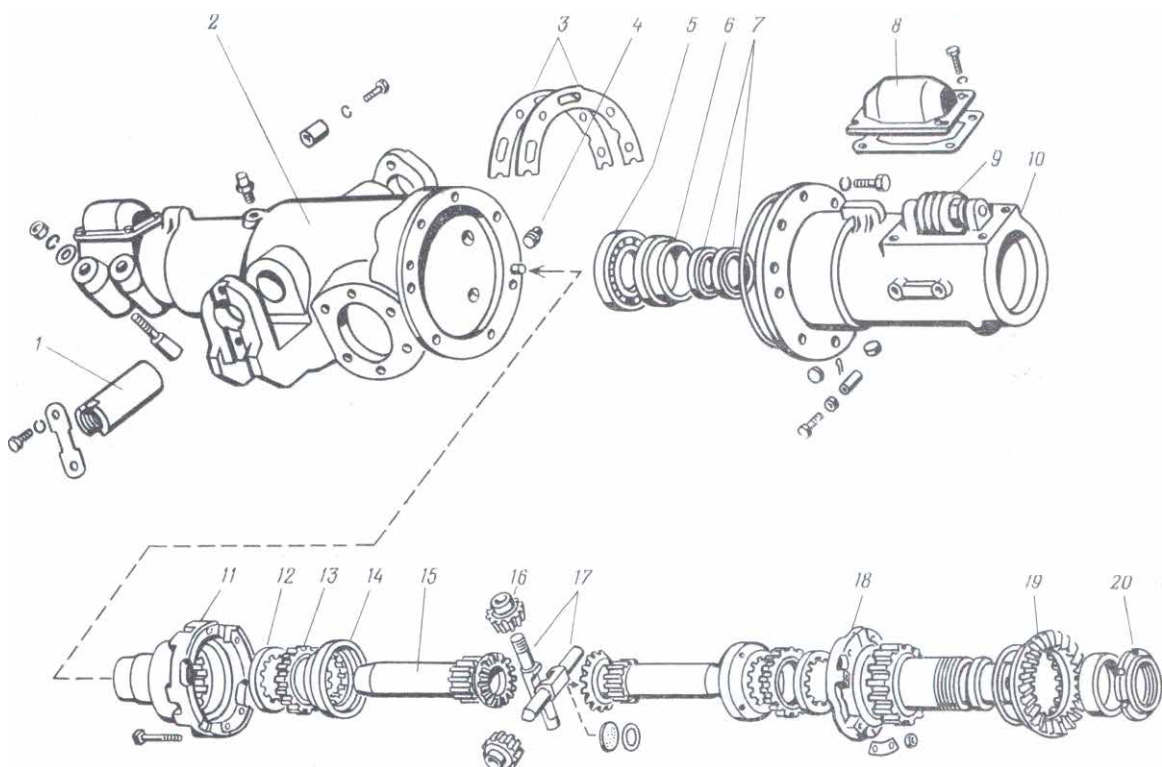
Взаємне розташування деталей корпусу, кришки і диференціала переднього ведучого моста: 1 - вісь; 2 - корпус; 3 - регульовальні прокладки; 4 - пробка; 5 - підшипник; 6 - обойма сальників; 7 - манжети; 8, 10 - кришки; 9 -
